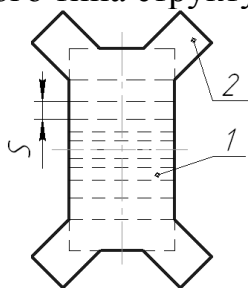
Эскиз исходной прессованной заготовки для отбора образцов под прокатку:
